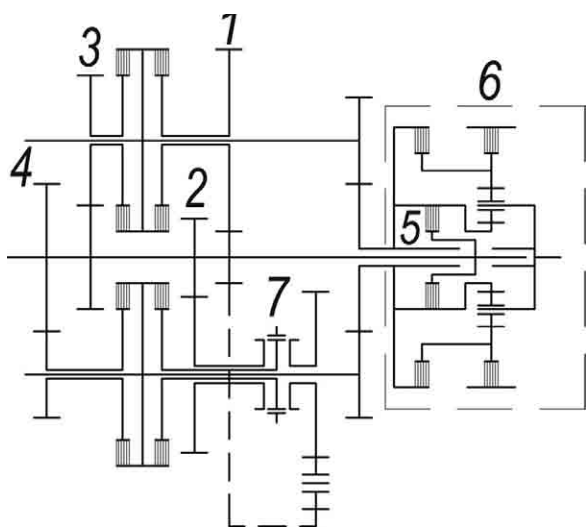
Кинематическая схема десятиступенчатой ГМП компании Allison Transmission, соответствующая конструкции ГМП ТС10: 1 — пара зубчатых колес первой и шестой передач; 2 — пара зубчатых колес второй и седьмой передач; 3 — пара зубчатых колес третьей и восьмой передач; 4 — пара зубчатых колес пятой и десятой передач; 5 — фрикционная муфта четвертой и девятой передач; 6 — демультипликатор; 7 — зубчатая муфта передачи заднего хода
